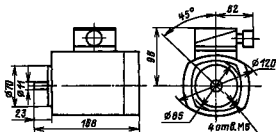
Габаритные и установочные размеры двигателя ДАТ 120-120-6
